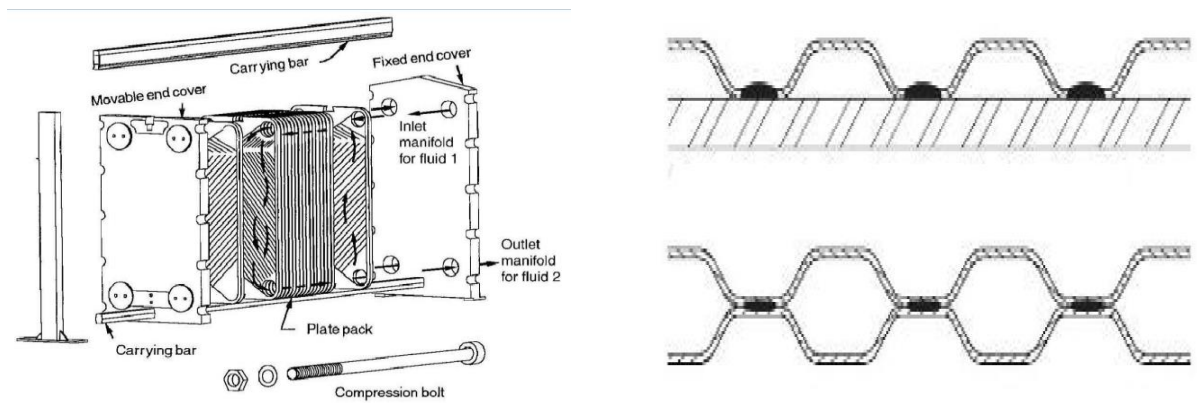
Echangeur de chaleur a joint étanche et a plaques soudées
